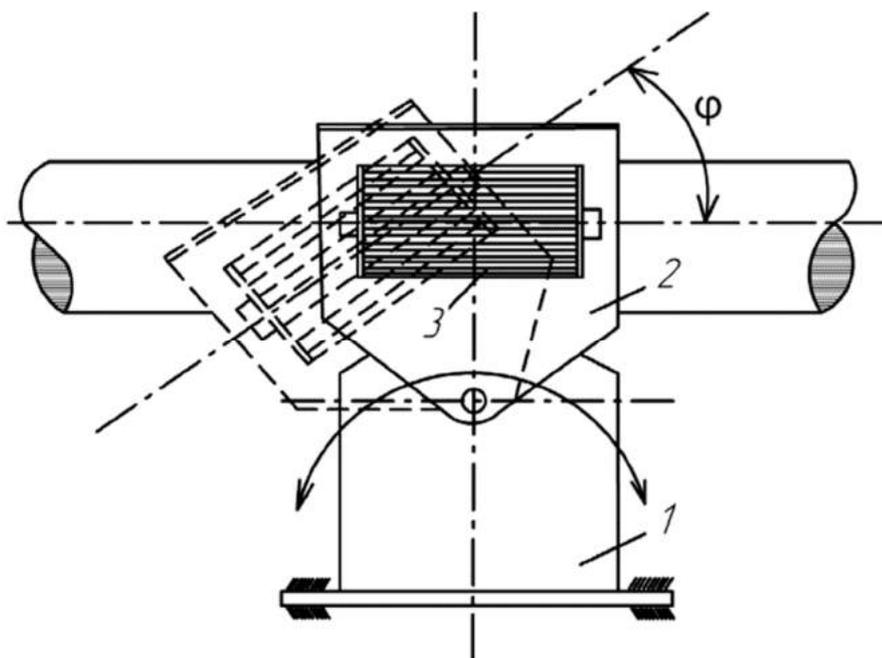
Фрезерная головка для доводки поверхности брёвен:
